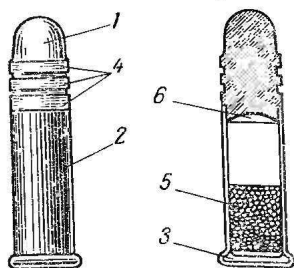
Малокалиберный патрон: 1 — пуля; 2 — гильза; 3 — закраина гильзы с ударным составом; 4 — ведущие пояски; 5 — пороховой заряд; 6 — сферическое углубление
